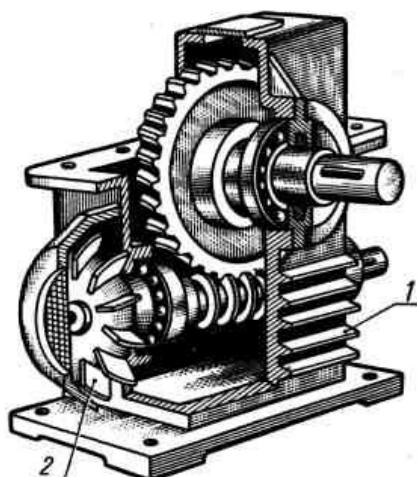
Способы охлаждения редуктора: 1 – ребра; 2 - вентилятор
